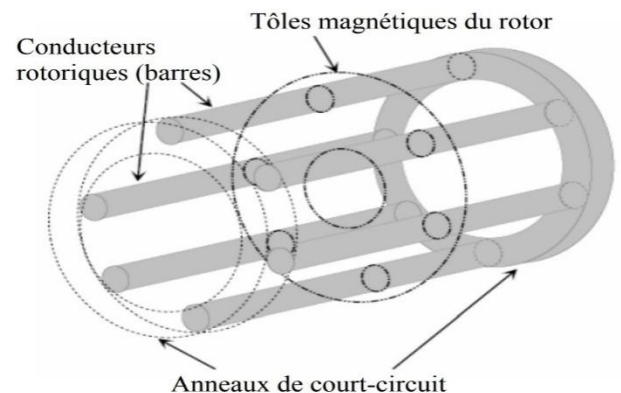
Vue schématique en Perspective du rotor [6].
